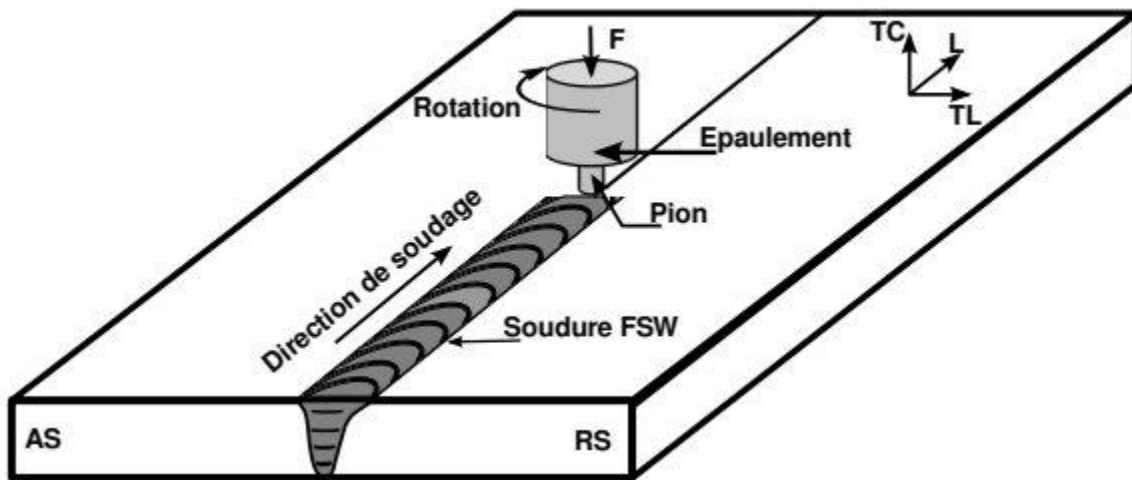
Paramètres du procédé de soudage par FSW [1].
